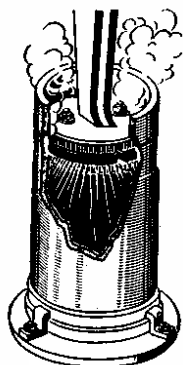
Гартування внутрішньої поверхні гільзи циліндра індуктором із залізним ланцюгом
